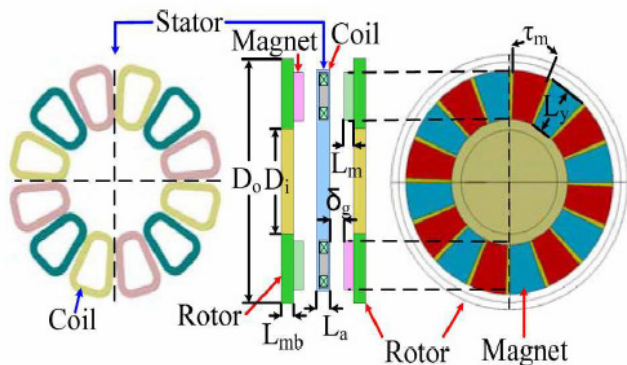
Machine à flux axial un stator et deux rotors avec bobinage sur dents [7]
